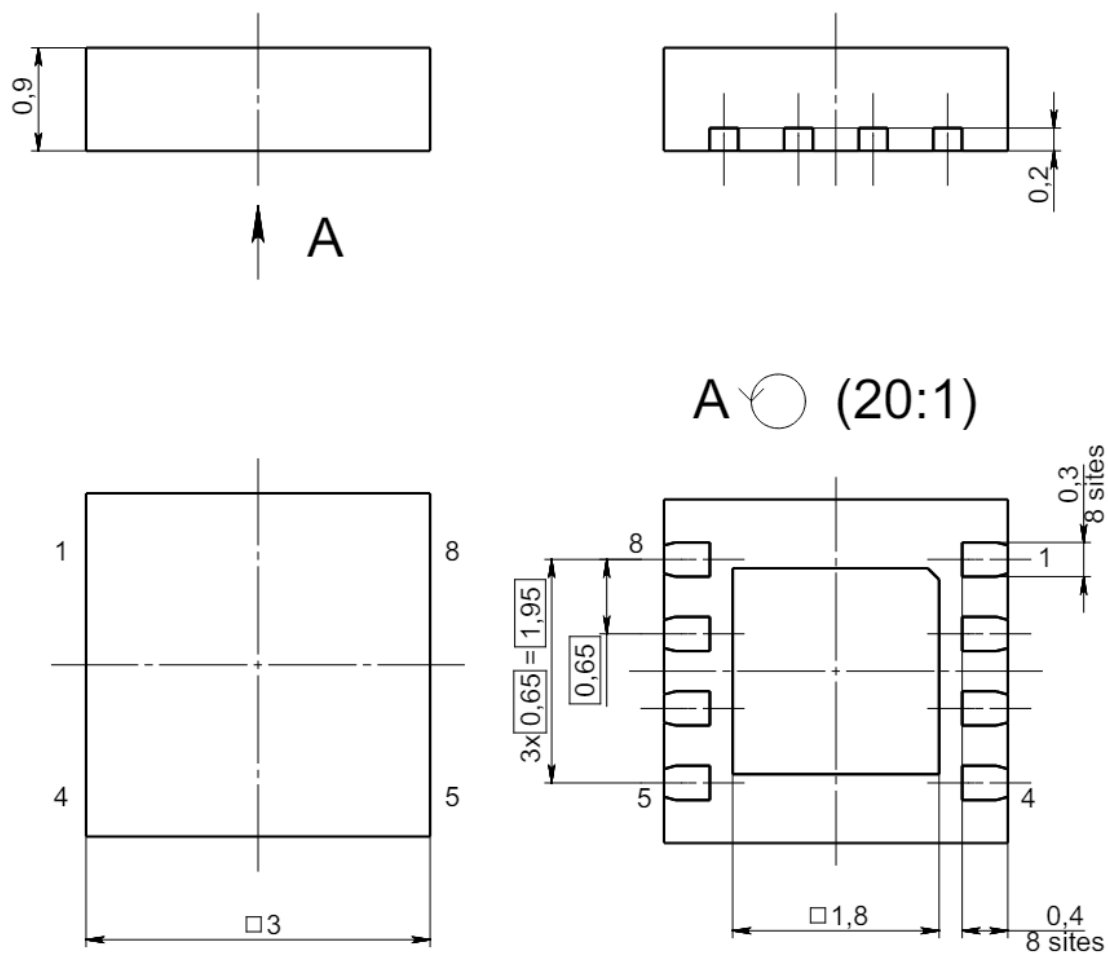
Габаритный чертеж корпуса 5241.8-1H3 K (размеры в мм)
